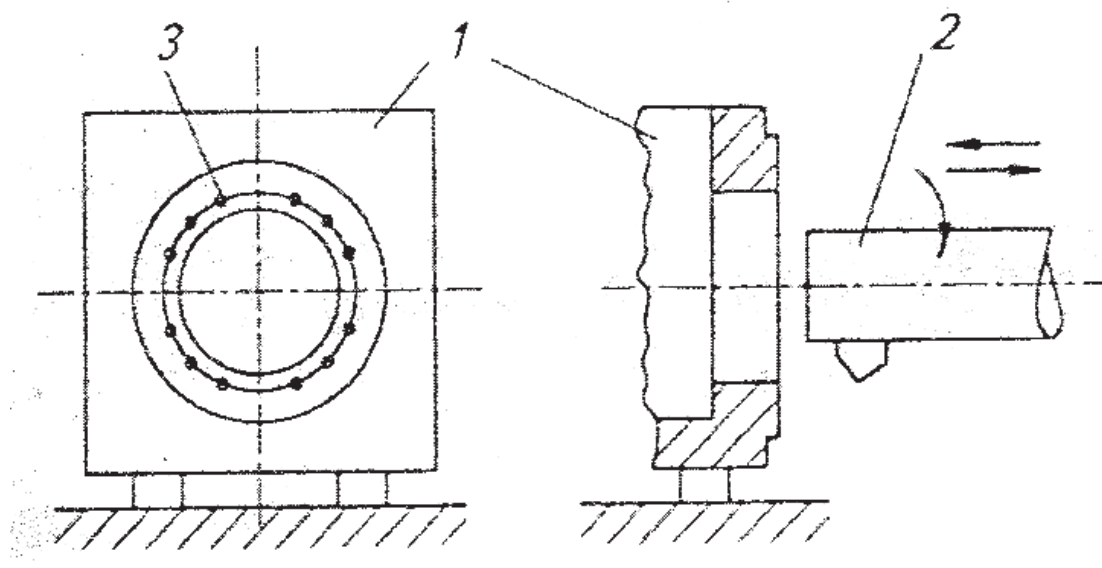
Схема расточки корпусной детали по разметке:
